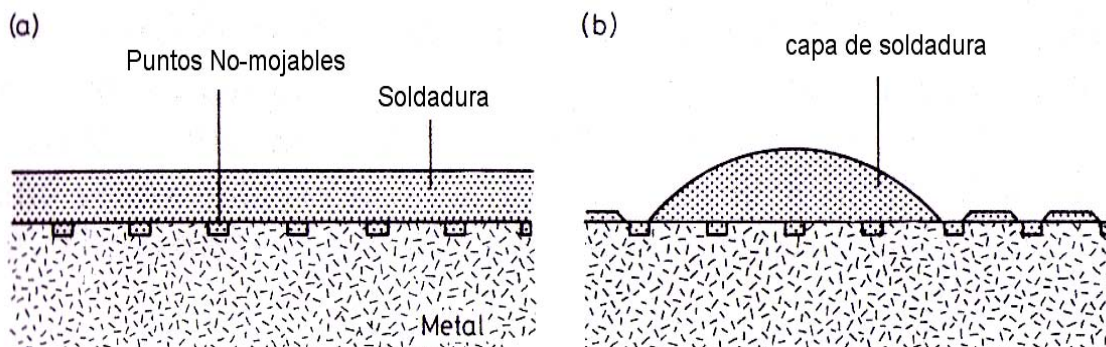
Superficies soldadas con defectos de mojado.
